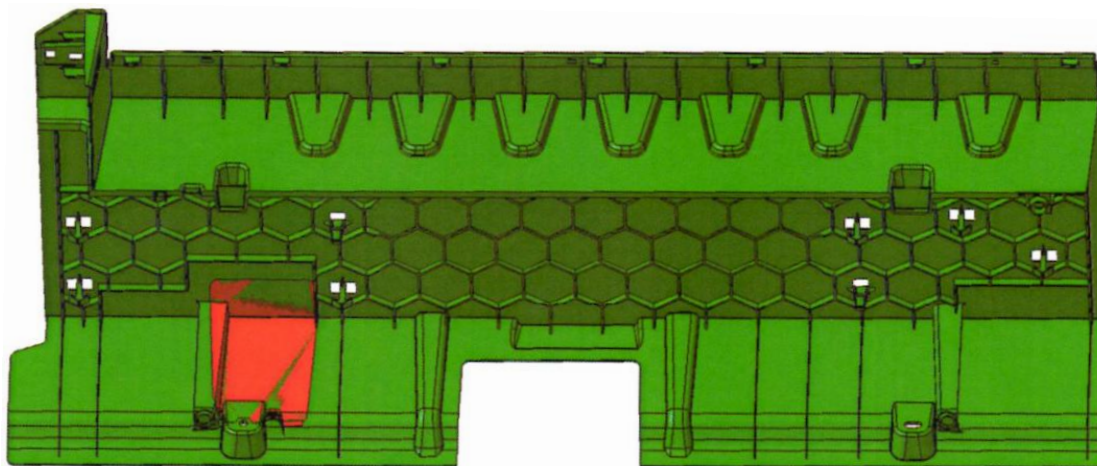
Superfícies da peça para o movimento à extração SI06.
